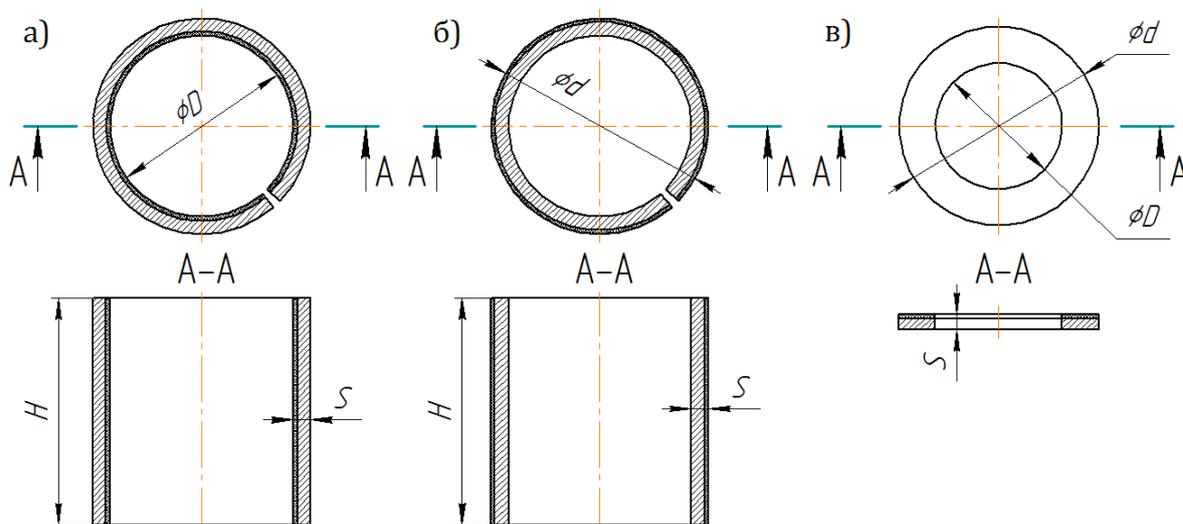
Общий вид: а – радиальный подшипник (направляющая) ТЕГ-8-В,
